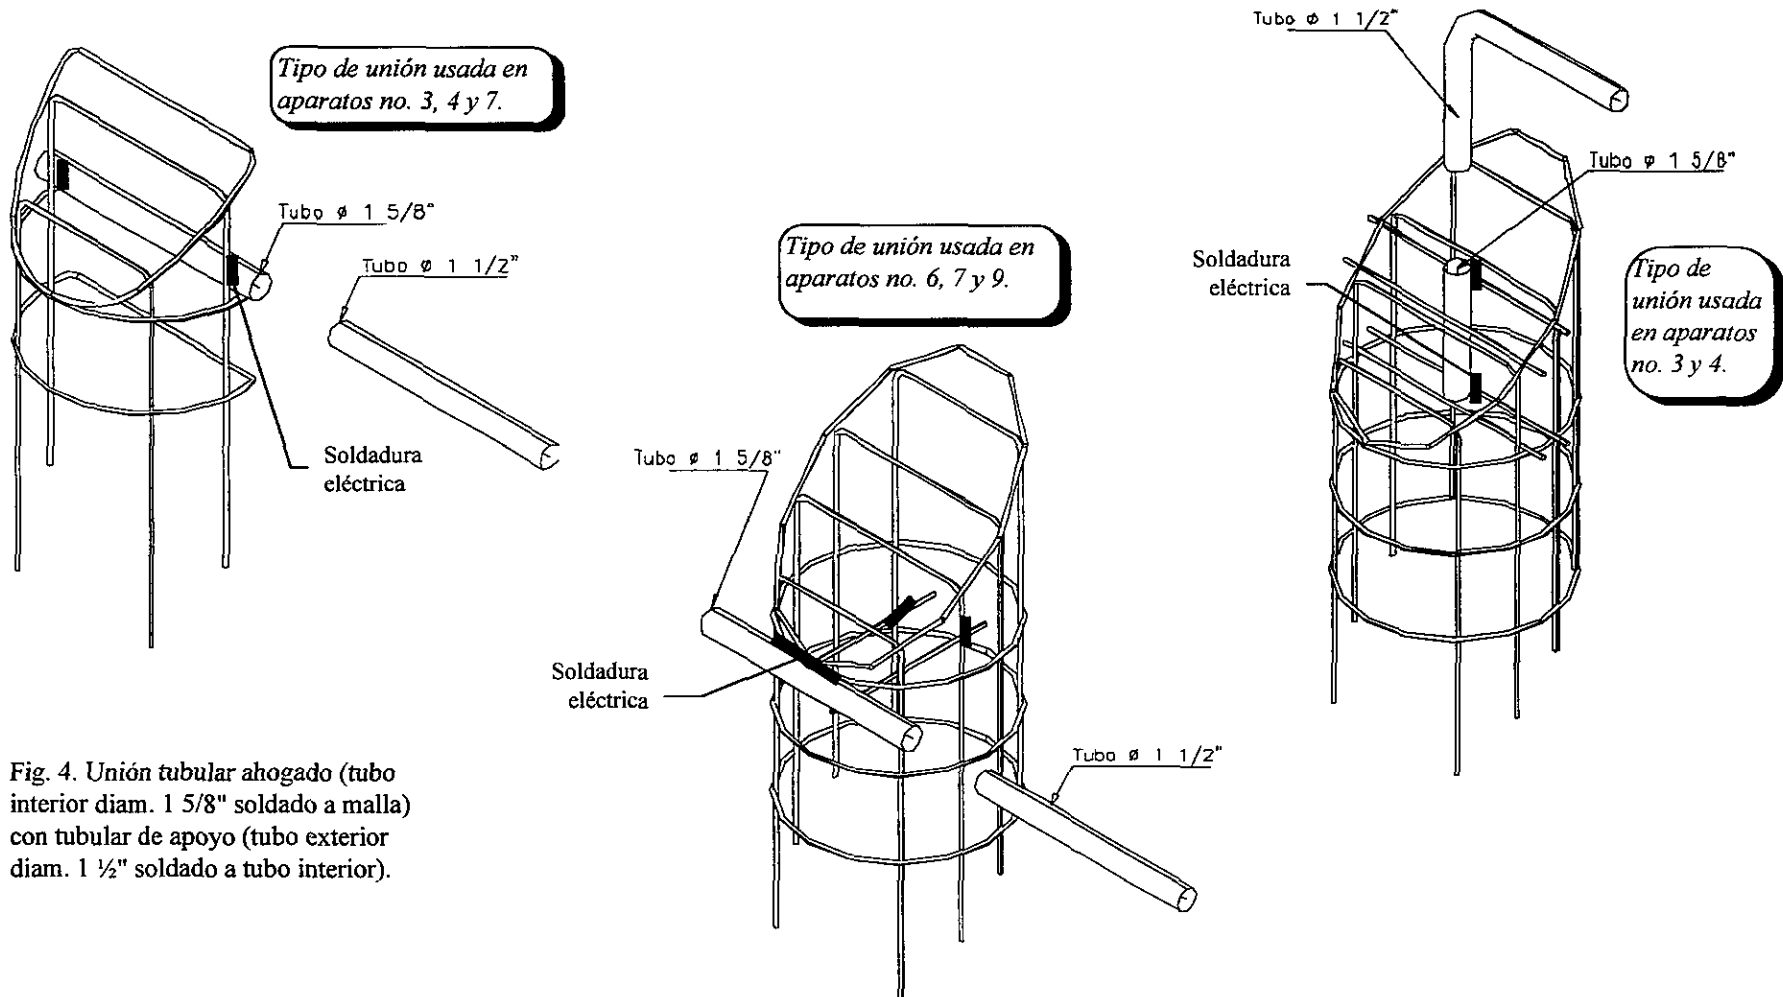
Unión tubular ahogado (tubo interior diam. 1 5/8" soldado a malla) con tubular de apoyo (tubo exterior diam. 1 ½" soldado a tubo interior).
